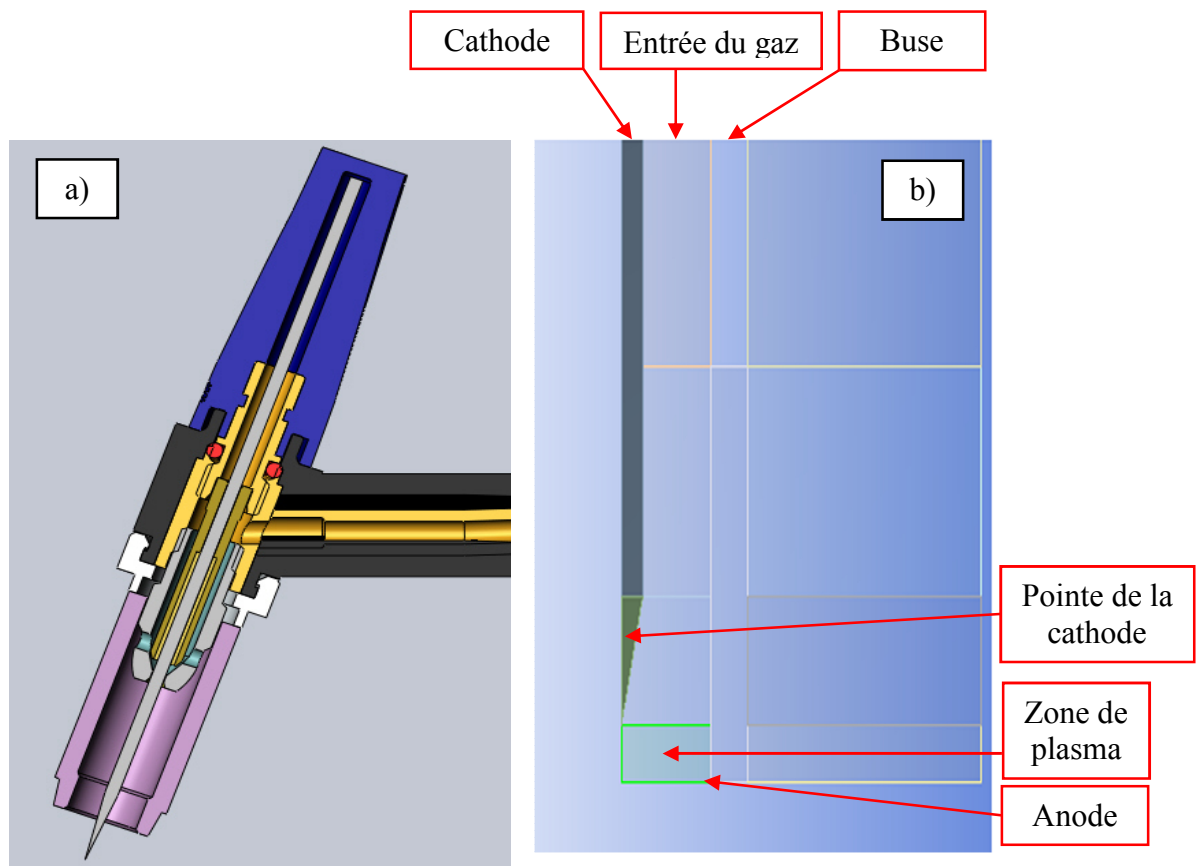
a) Torche de soudage - b) Electrode
